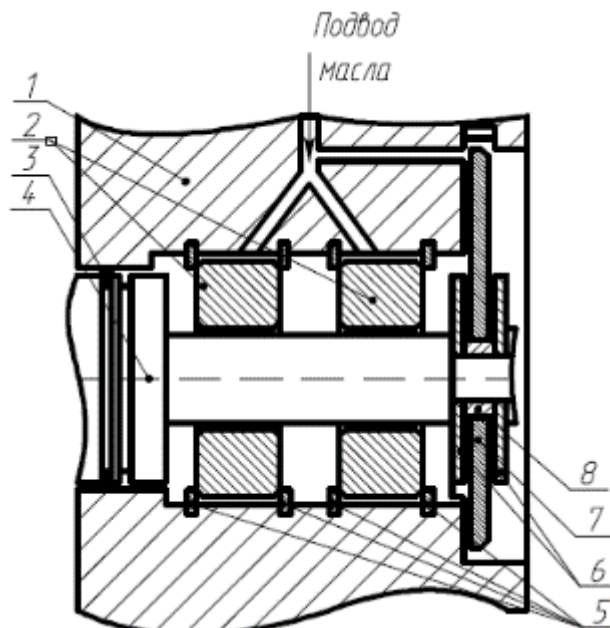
Підшипниковий вузол з обертовими втулками
